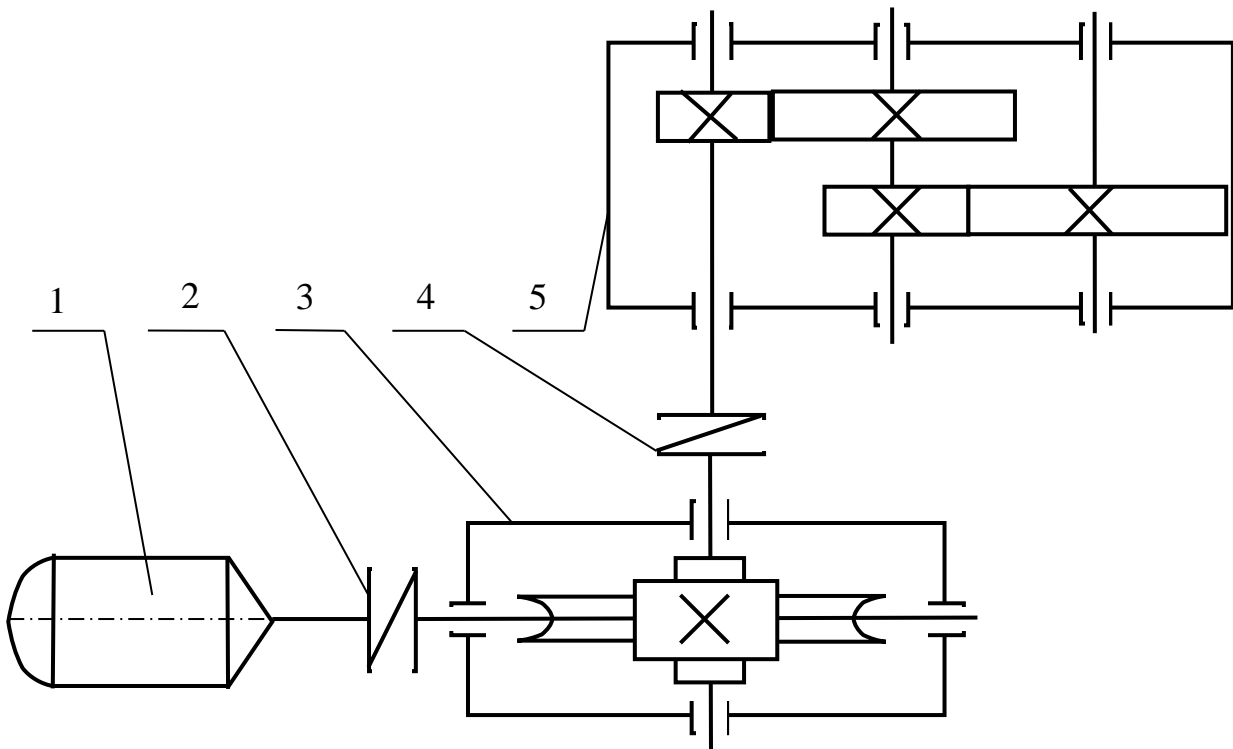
Схема лабораторной установки с цилиндрическим редуктором:
